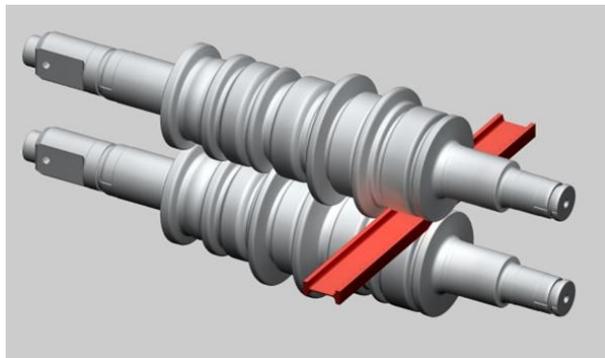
Cilindros do laminador debastador de perfis estruturais.
